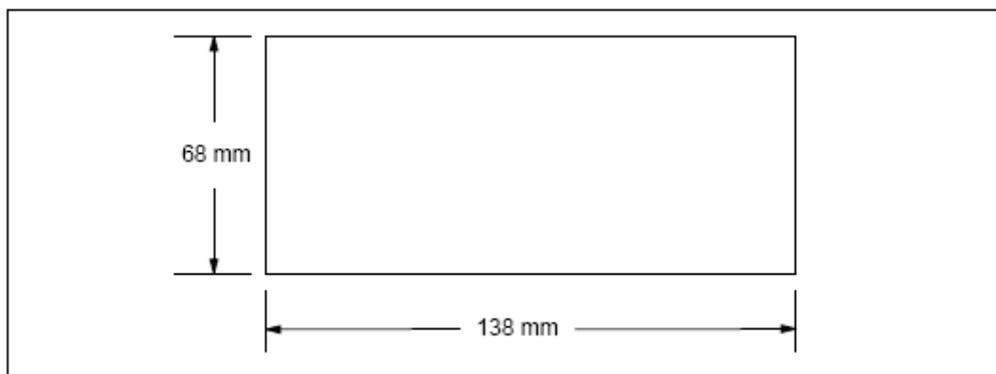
Dimensiones del Recorte en la superficie de montaje.
